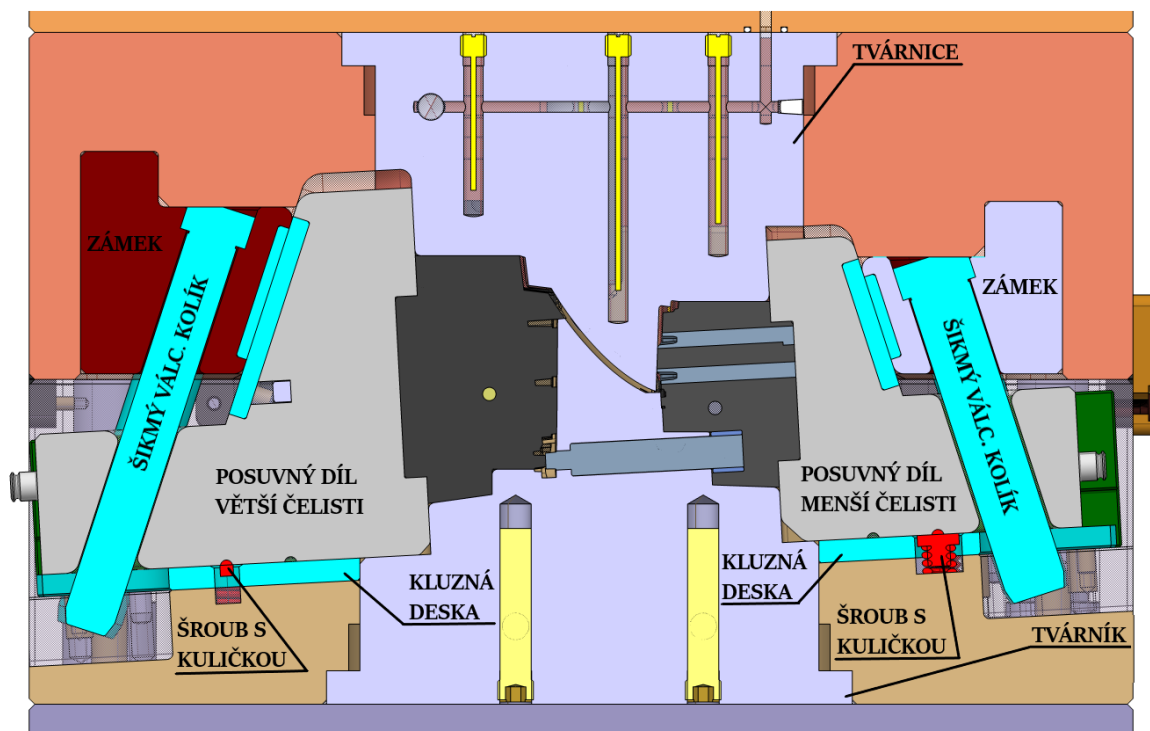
Kompletní sestava bočních posuvných čelistí v uzavřeném stavu
